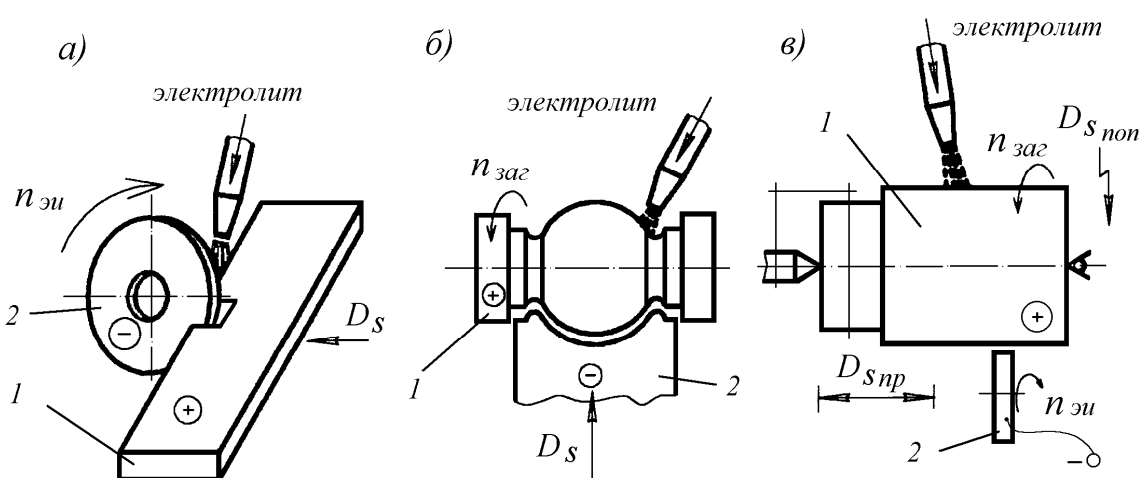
Схемы анодно-механической резки (а), анодно-механического фасонного точения (б) и анодно-механического точения цилиндрической поверхности (в): 1 — заготовка; 2 — электрод-инструмент
